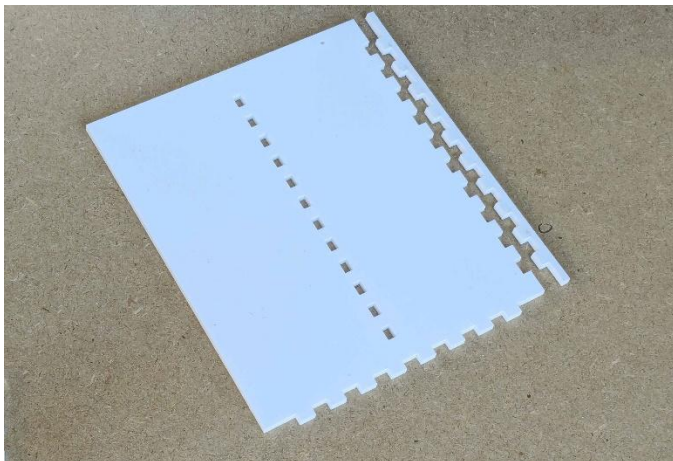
Montage des supports de glissières de la trappe arrière sur un côté
